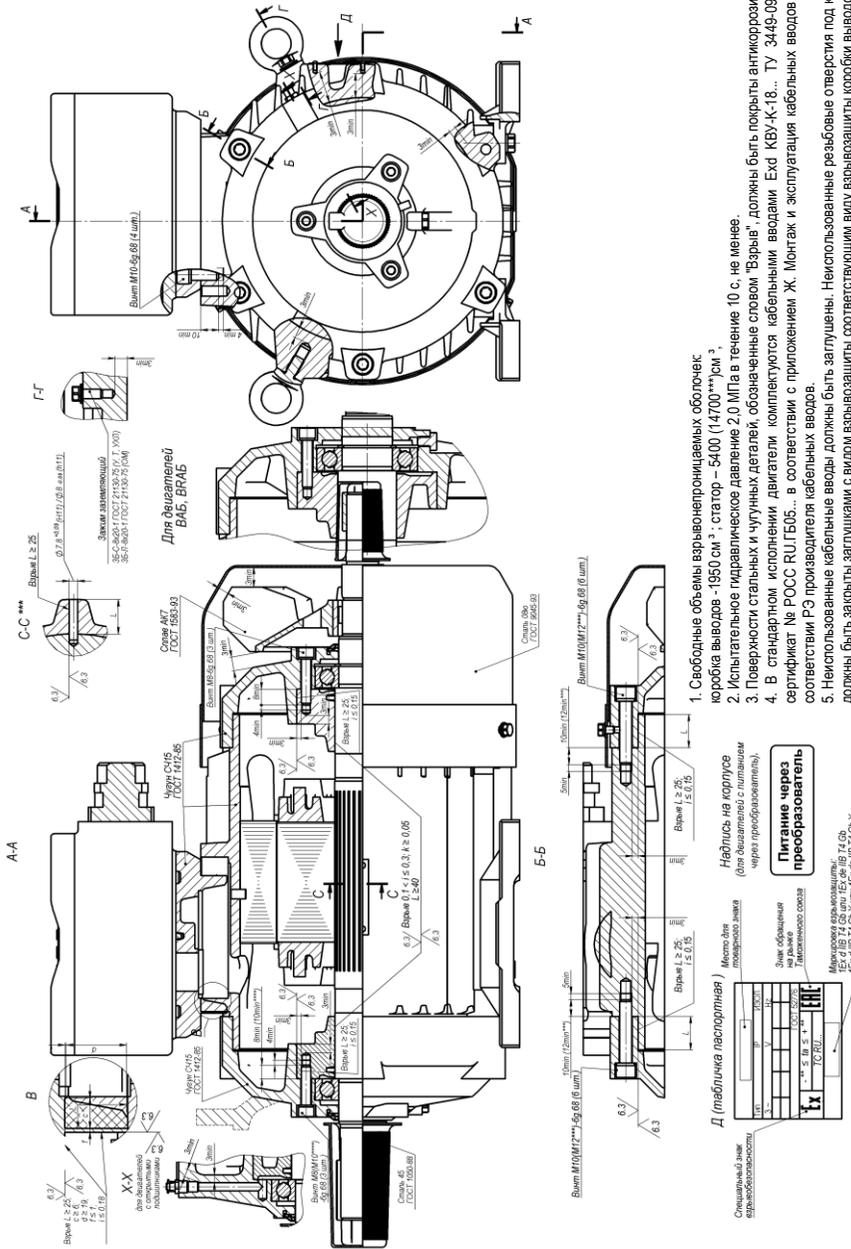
Чертеж взрывозащиты двигателя
